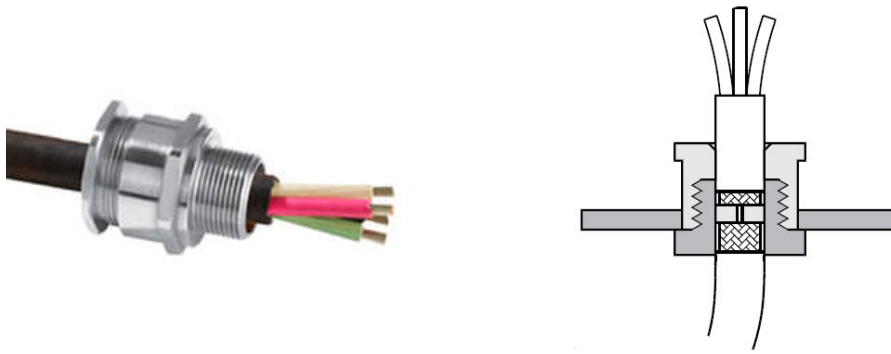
Passacables metàl·lic. (esq.). Vista esquemàtica de la secció d'un passables (dreta).
